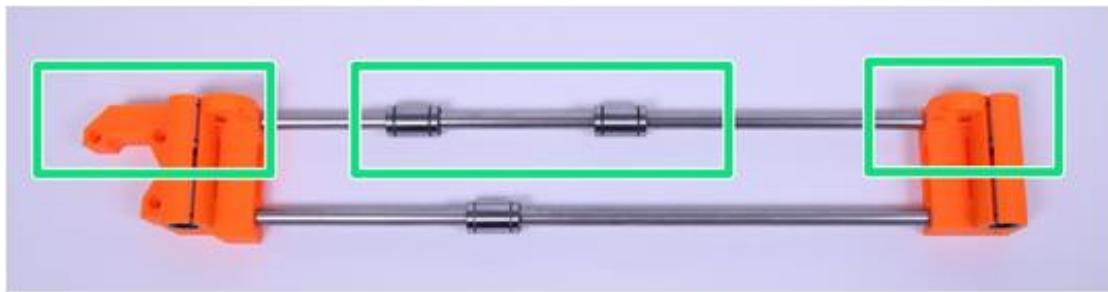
Ensamblaje del eje x; Fuente: Manual de montaje
